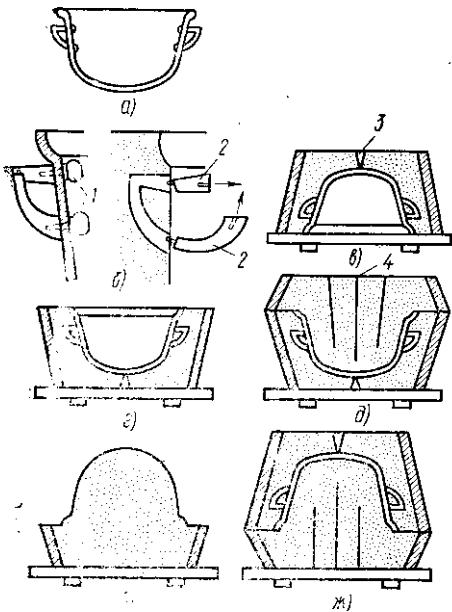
Формовка по модели с отъемными деталями (в разрезе):
